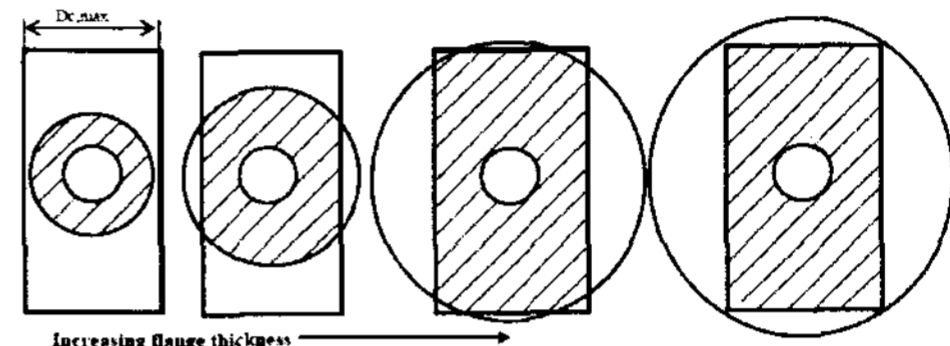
flange t에 따라 응력을 받는 면적 변화
